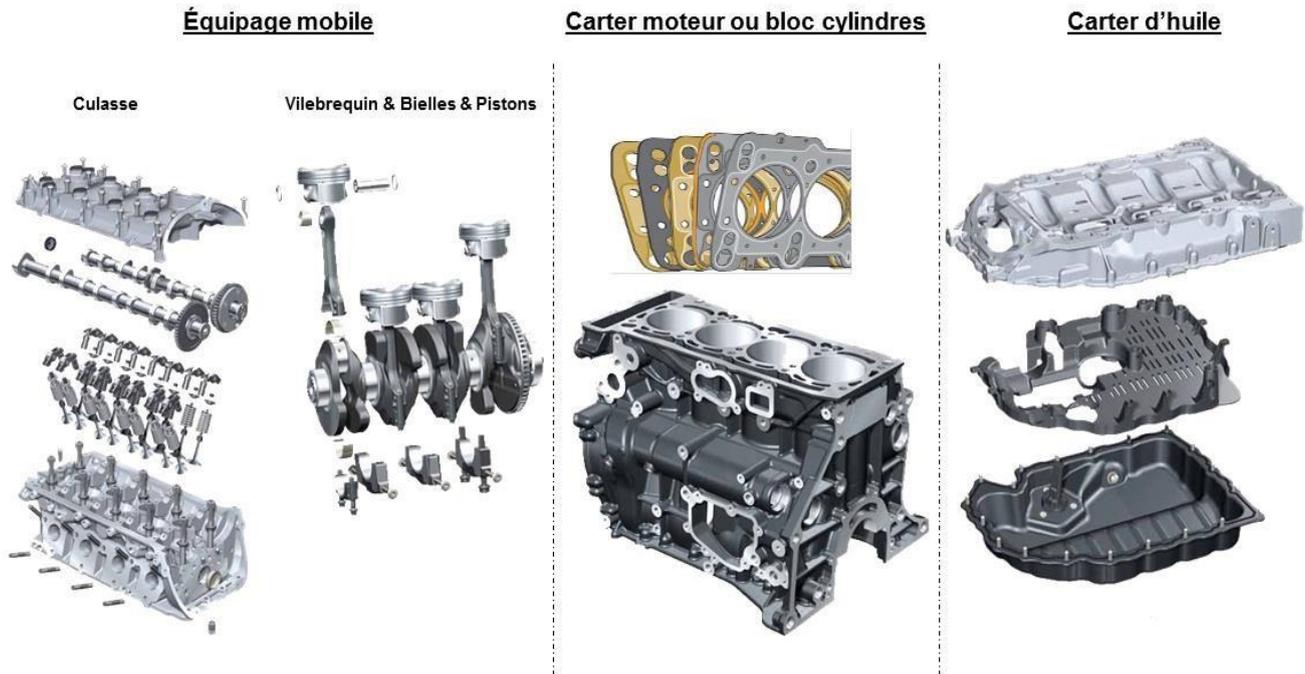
Vue éclaté d'un moteur à combustion interne [4]
